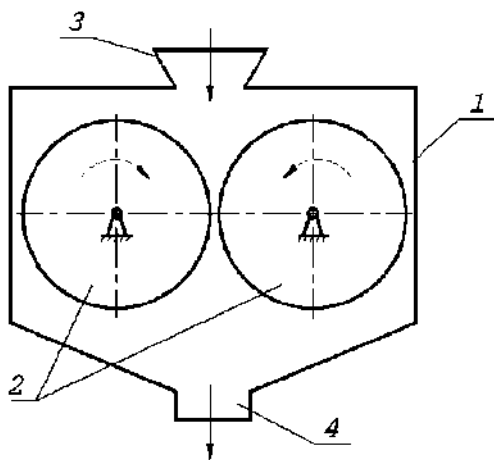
Валковий перероблювальний пристрій з гладкими поверхнями валків
